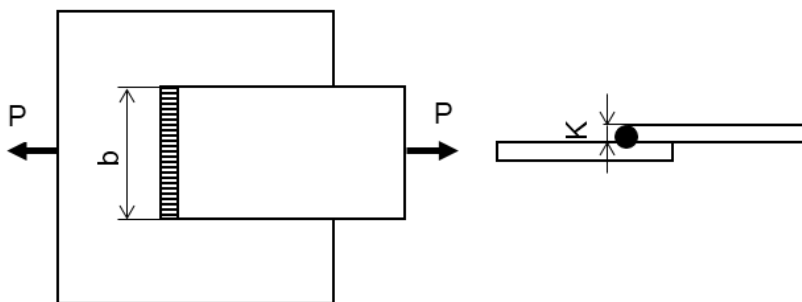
До розрахунку лобового внапуск зварного шва
